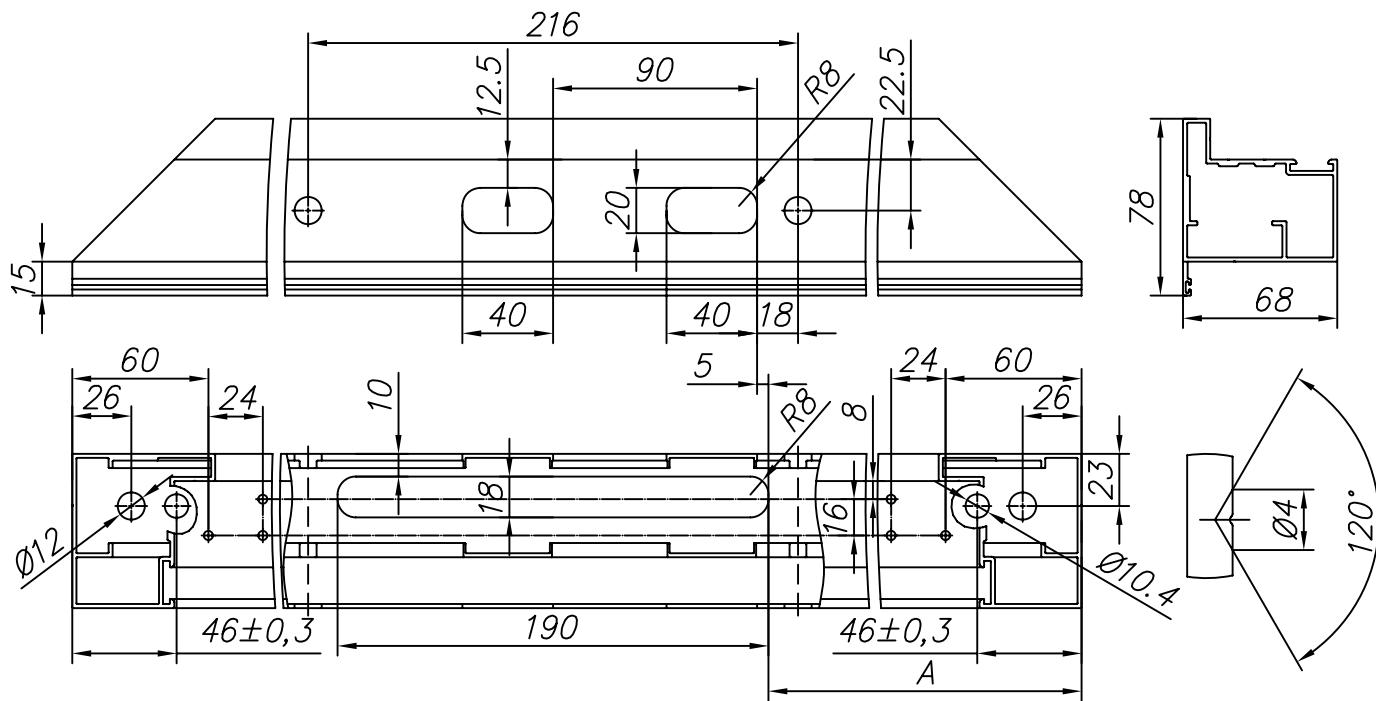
Изготовление стойки с пазом для замка из профиля FLGU.400.0108 (открытие наружу, влево)
